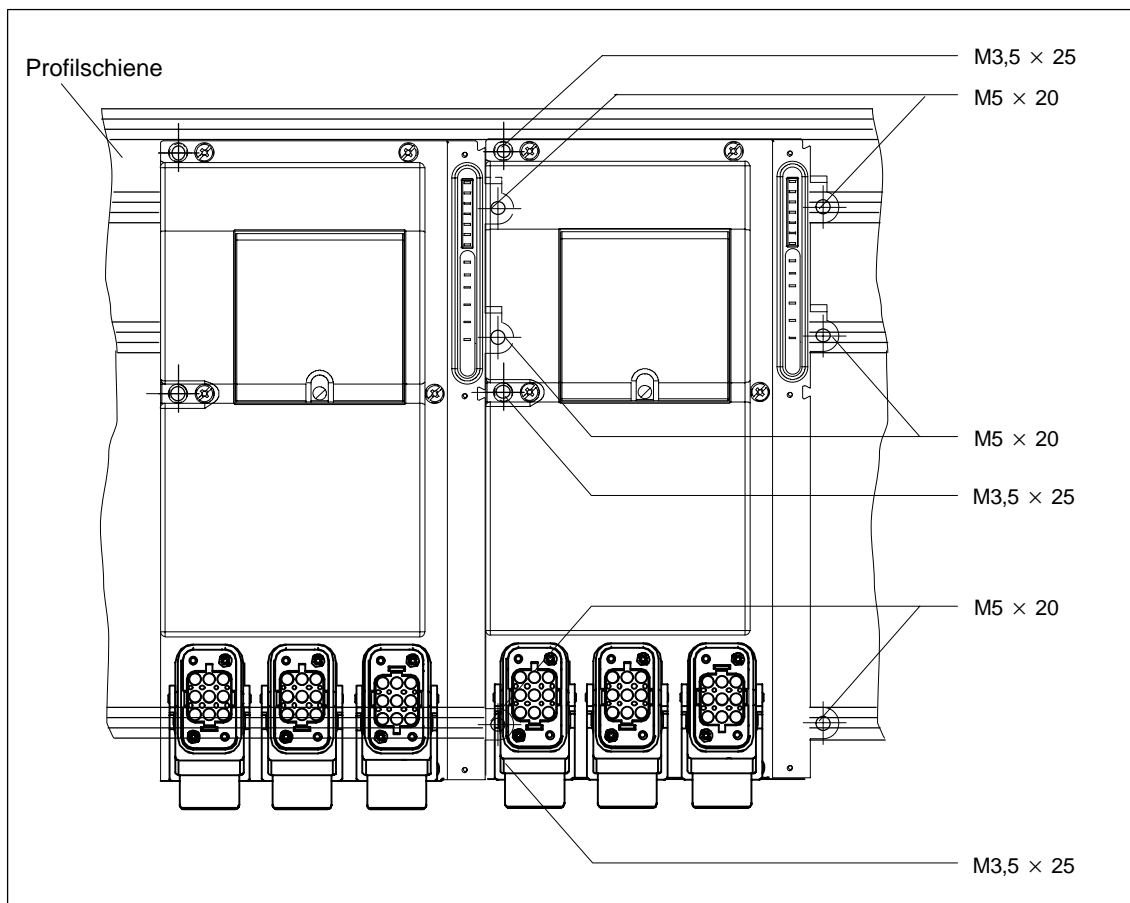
Befestigungsschrauben für Motorstarter bzw. Frequenzumrichter
